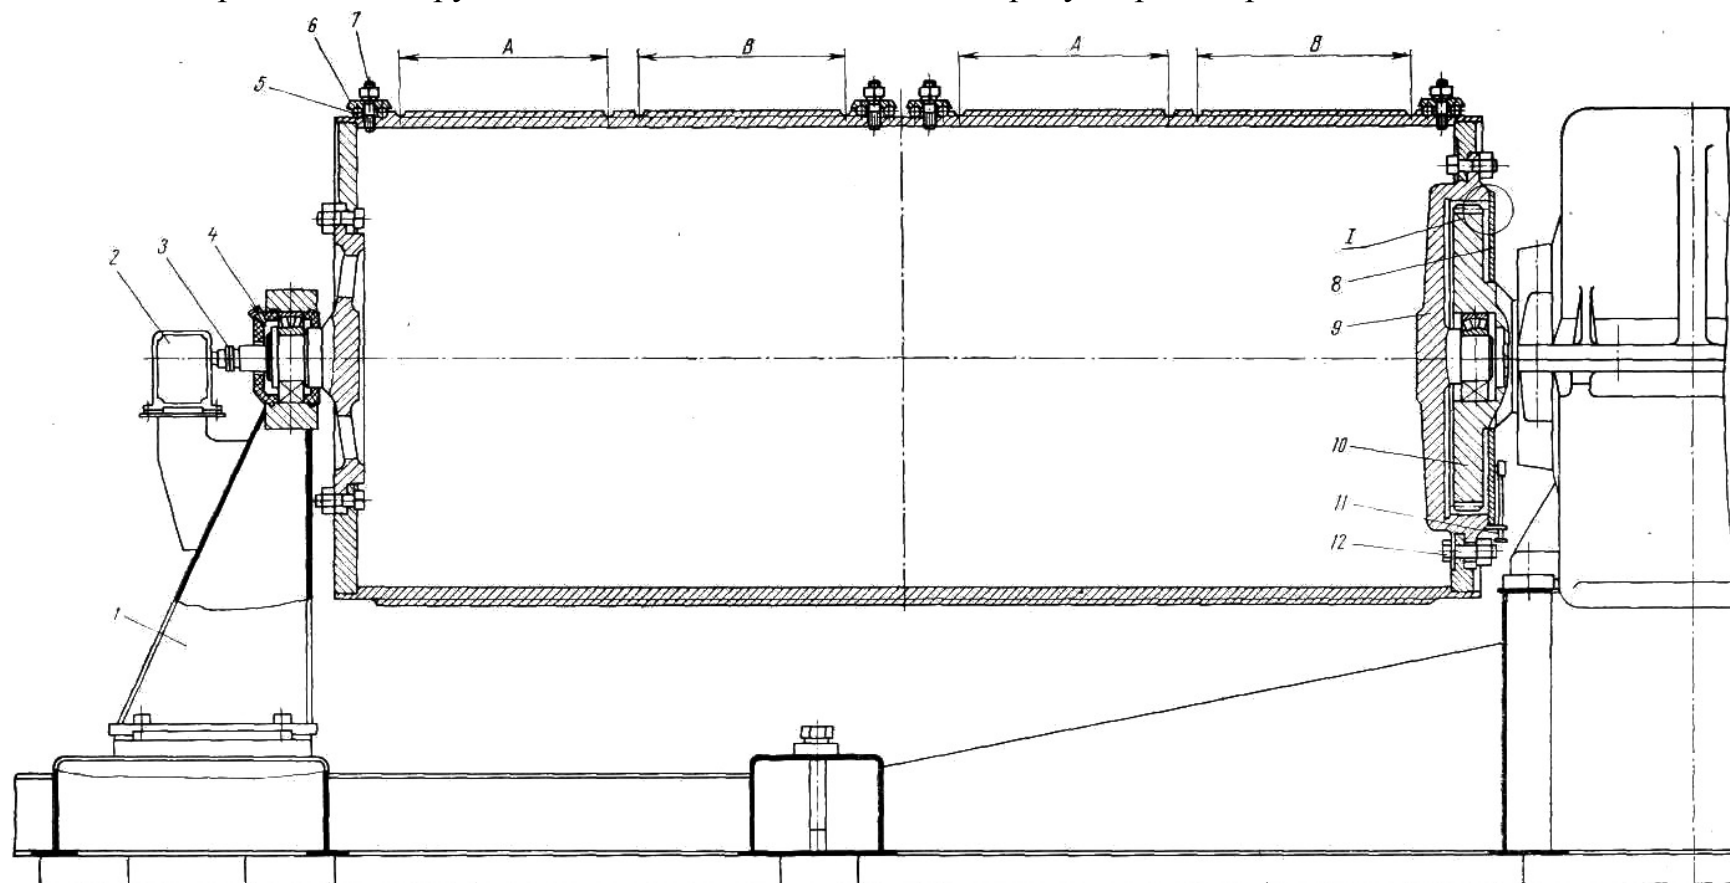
Безосное конструктивное исполнение соединения редуктора и барабана механизма подъема:
